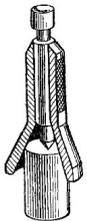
Приспособление (колокол) для накернивания центрального отверстия без разметки
